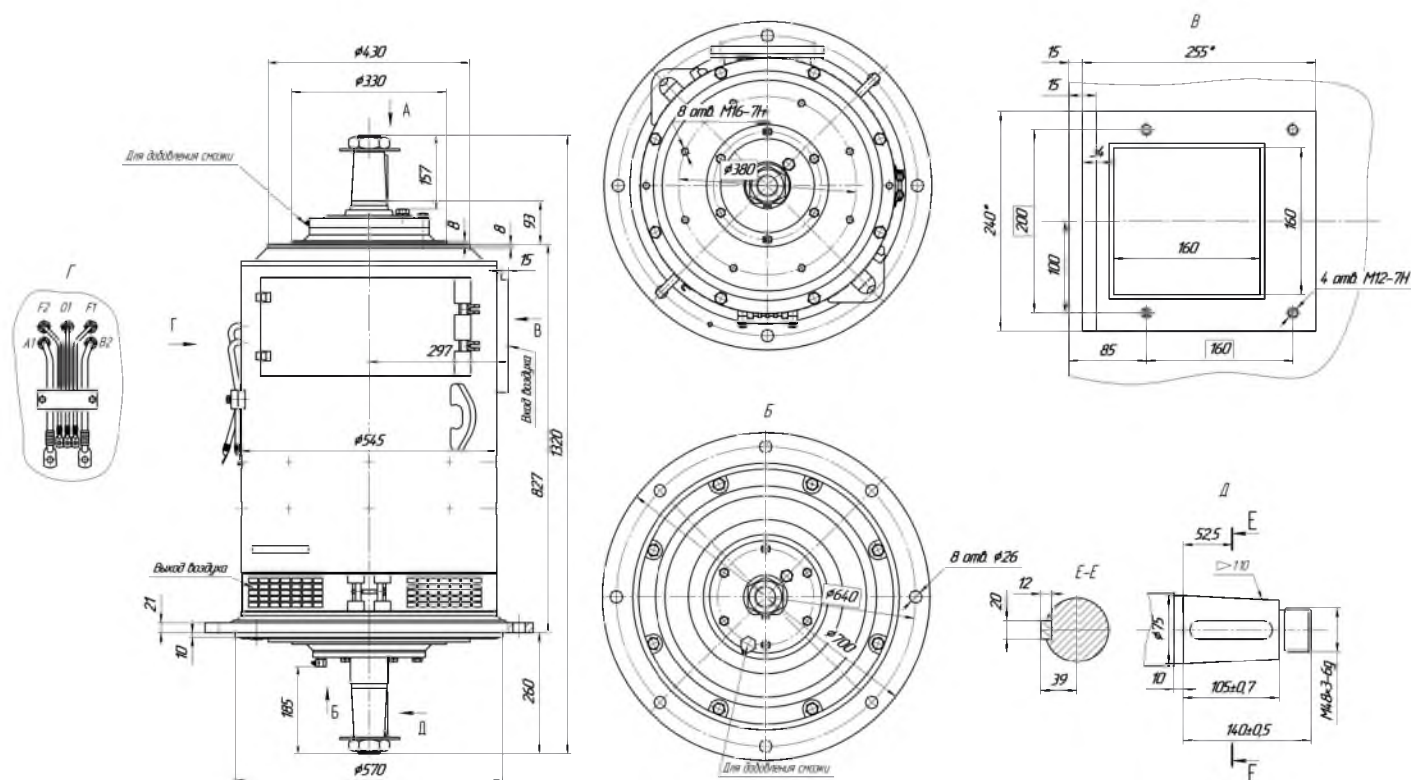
Габаритно-установочные размеры экскаваторного электродвигателя ДПВ-52М
